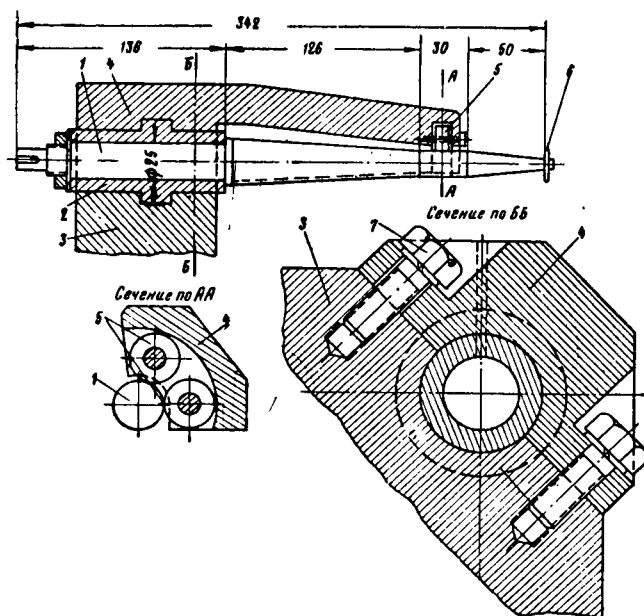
Конструкция шпинделя приспособления для продорожки коллекторов:
